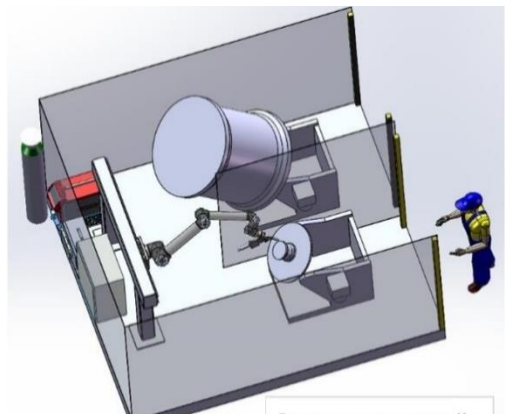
Aperçu de la proposition cobot de FTS Welding
